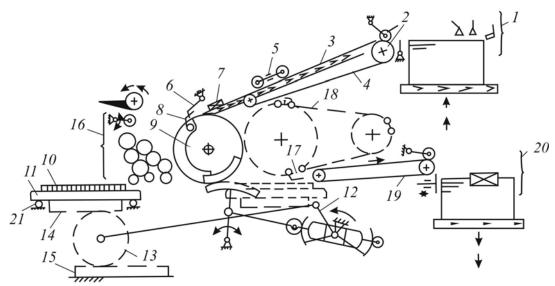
Принципиальная схема однооборотной плоскопечатной машины: 1 — листопитающее устройство; 2 — приемные ролики; 3 — наклонный стол; 4, 19 — тесемочные транспортеры; 5 — грузовые ролики; 6 — передние упоры; 7 — боковой упор; 8 — захваты печатного цилиндра; 9 — печатный цилиндр; 10 — форма; 11 — талер; 12 — кривошип; 13 — шестеренчатый скат; 14, 15 — зубчатые рейки; 16 — красочный аппарат; 17 — захваты листовыводного транспортера; 18 — цепной листовыводной транспортер; 20 — приемное устройство; 21 — роликовые подвижные опоры
